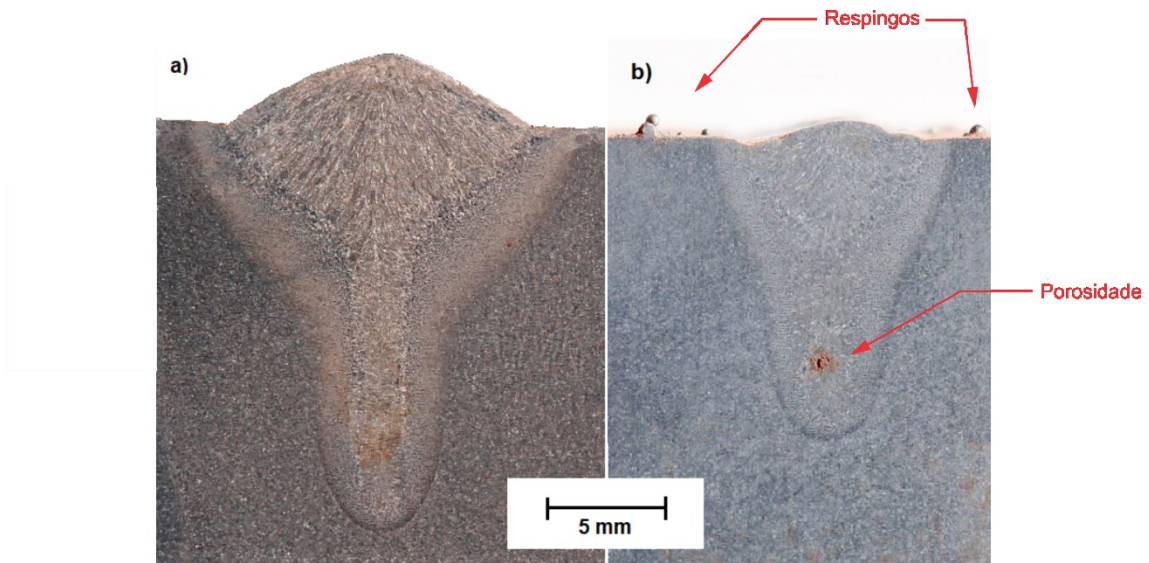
Macrografias das seções transversais dos cordões de solda obtidos através dos processos de soldagem HLAW (a), e soldagem Laser (b), ambos com 8 kW de potência Laser e 1 m/min de velocidade de soldagem. (Fonte: Autor)
